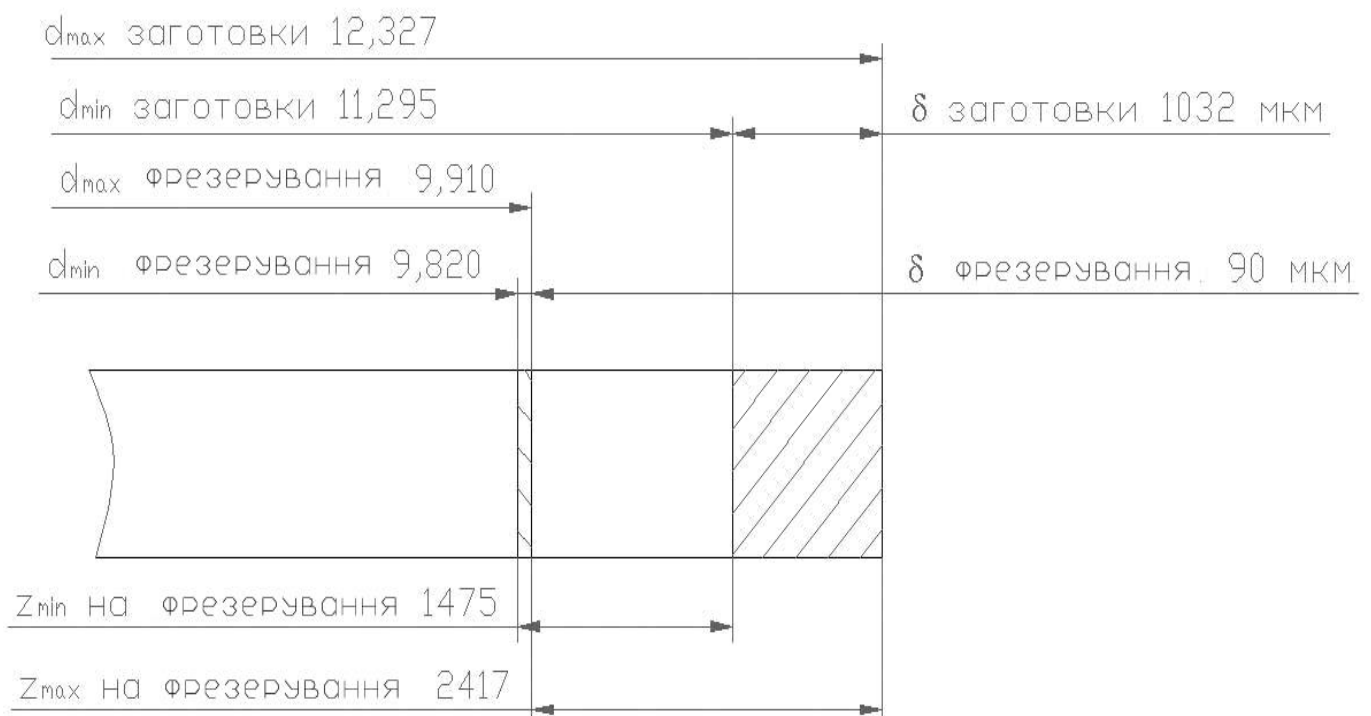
Схема графічного розташування припусків і допусків на обробку торців шатуна
